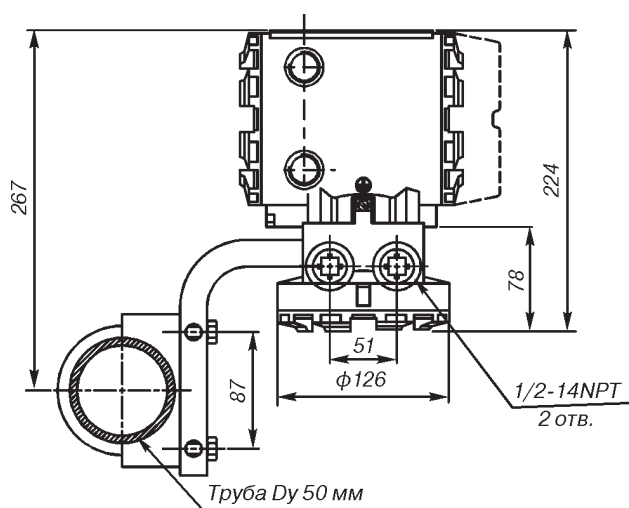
Габаритные и присоединительные размеры преобразователя 8732Е, удаленный монтаж на трубе Ду 50.
